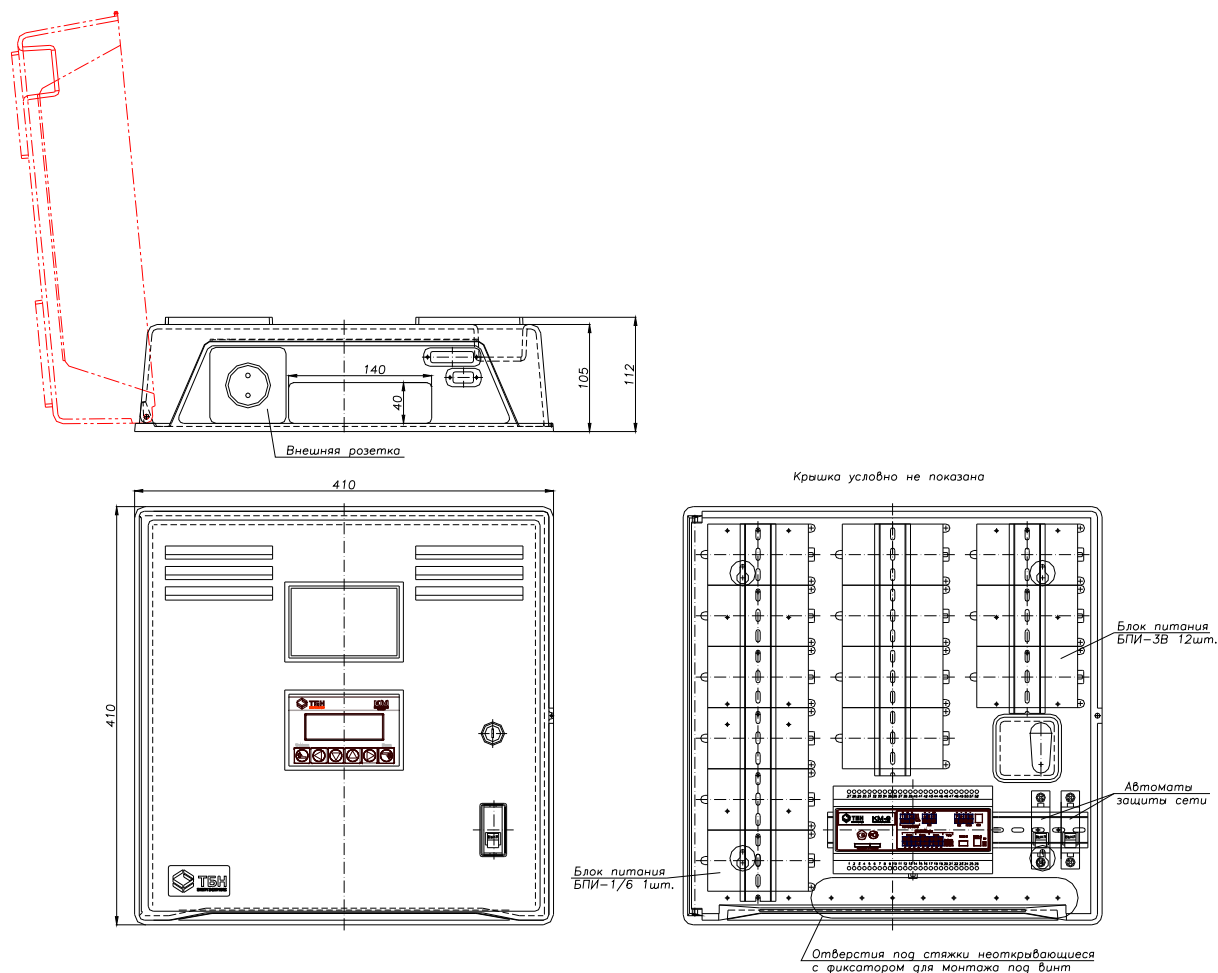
Габаритный чертеж щита монтажного КМ-9
